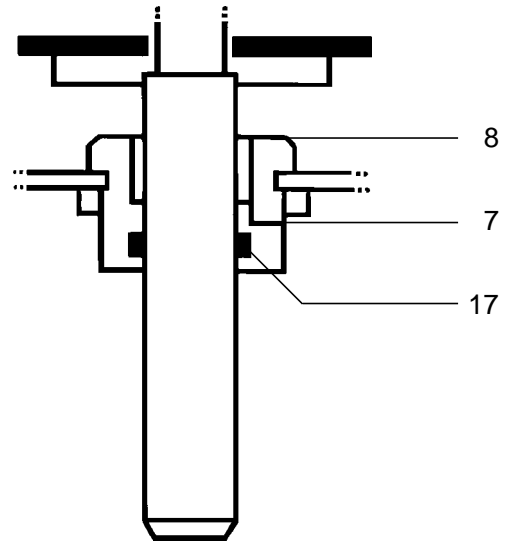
Series PN 5500, PN 5600, PN 6500 y PN 6600
